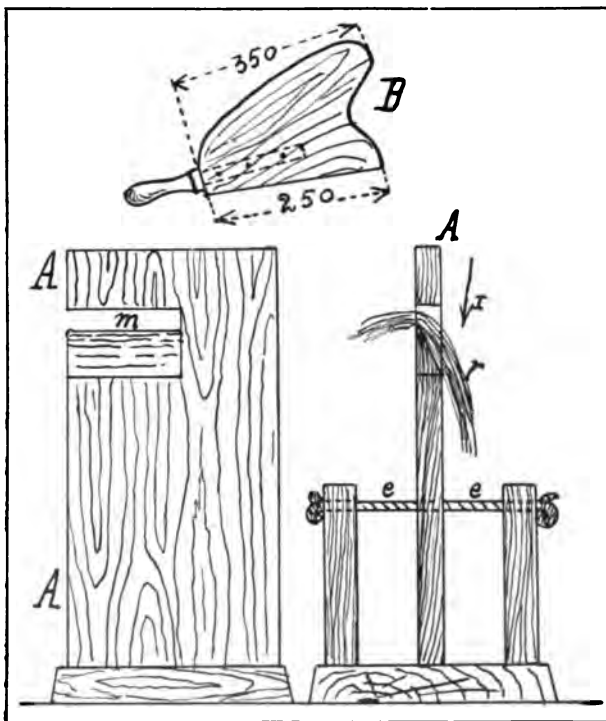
, 22 u. 23. Handschwingstock mit Schwingbeil.
